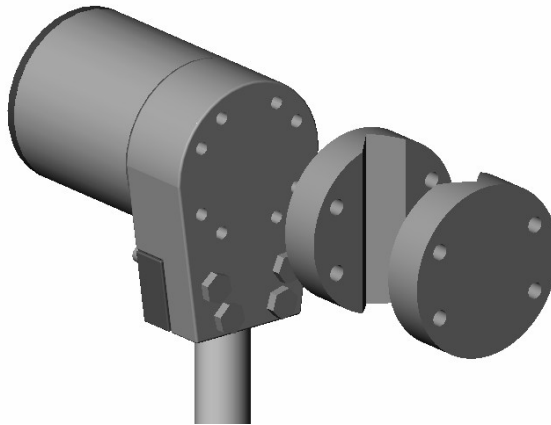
Rimozione dei blocchetti di fissaggio della barra di montaggio
